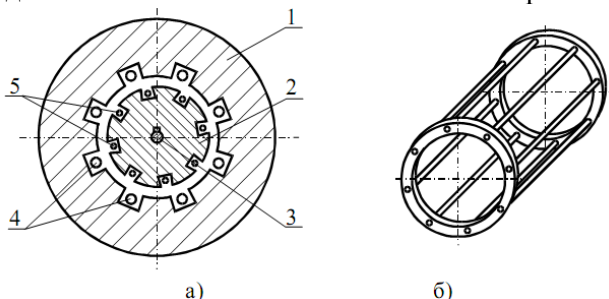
Схема пристрою асинхронного двигуна: поперечний розріз (а); обмотка ротора (б)
